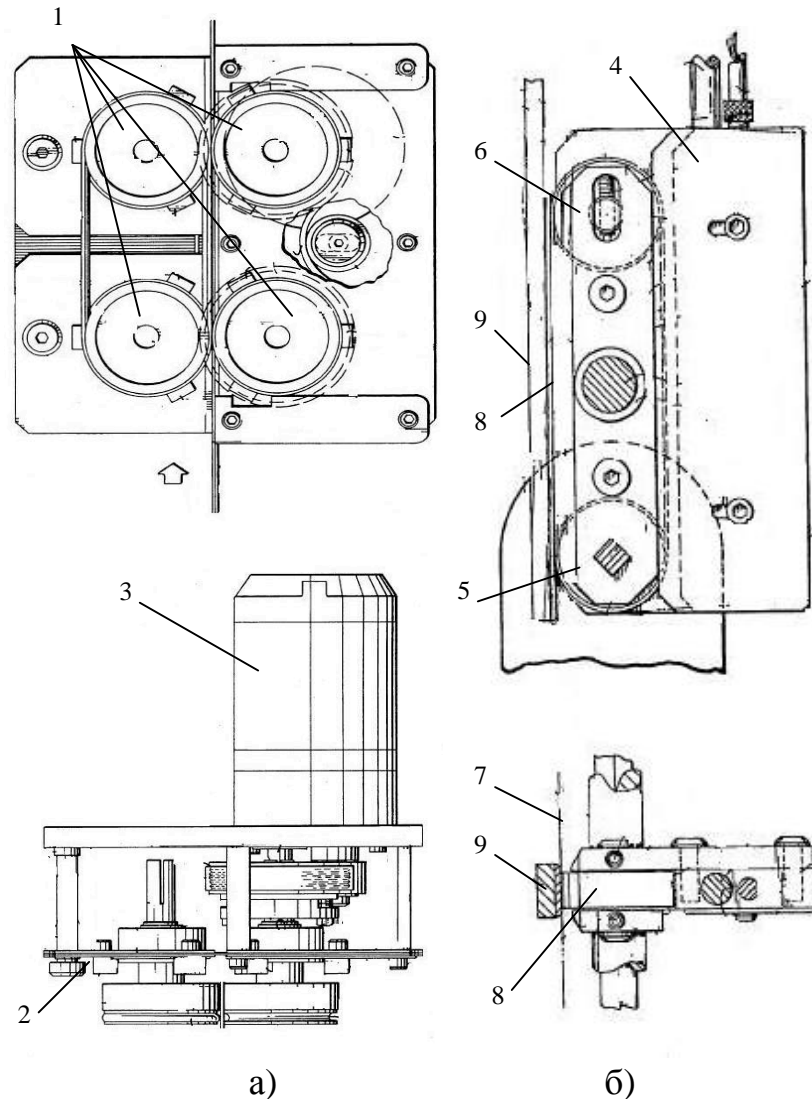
Механізми поздовжнього зварювання: а) стрічковий; б) роликовий
